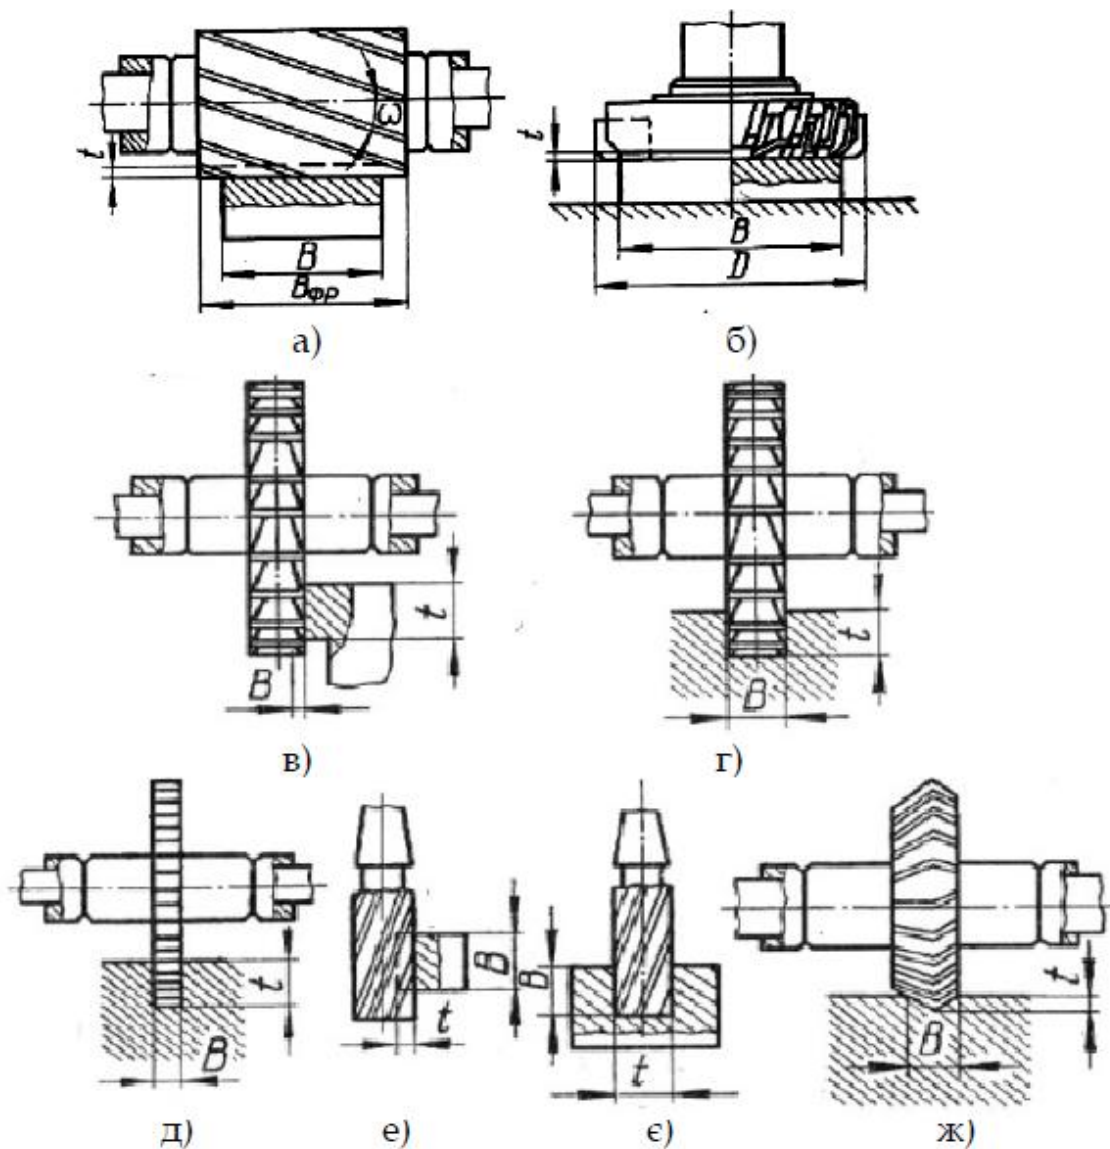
Типи фрез: а – циліндричні; б – торцеві; в, г – дискові; д –
